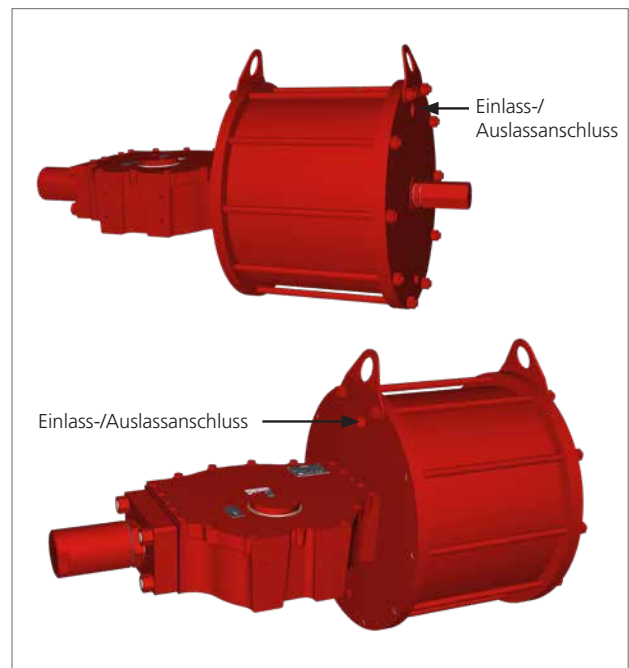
Ein- und Auslassanschluss für doppelt wirkenden Stellantrieb
